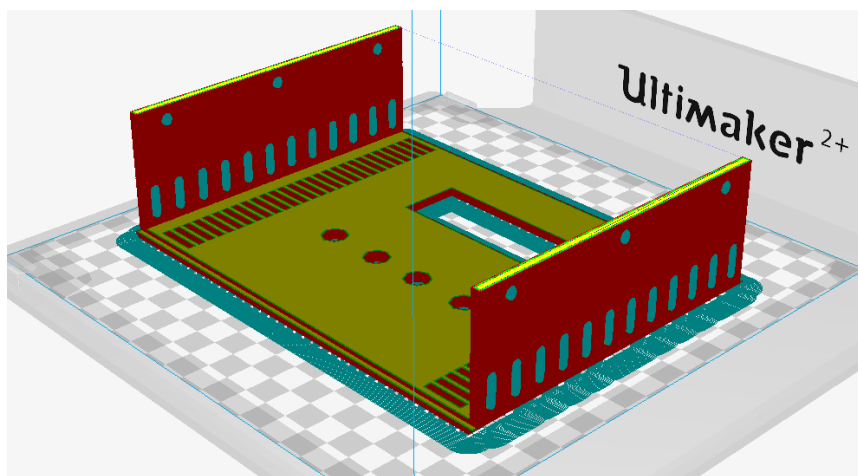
Процесс нарезки на слои верхней крышки корпуса
